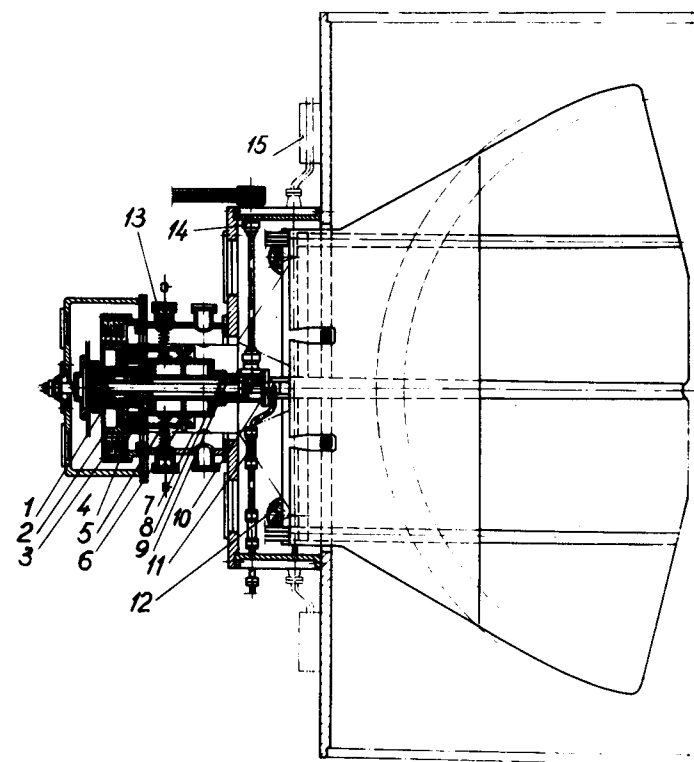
Общий вид ВЧ системы ускорителя. 1 - подшипники, 2 - ротор, 3 - статор, 4 - токосъемное кольцо, 5 - пружины опорные, 6 - опорный изолятор, 7 - наружная труба резонансной линии, 8 - вал ротора, 9 - подшипники, 10 - редуктор, 11 - водопровод для охлаждения ротора, 12 - несущие опоры балок дуанта, 13 - изолятор пружин, 14 - карданный вал, 15 - стенд водоохлаждения.
